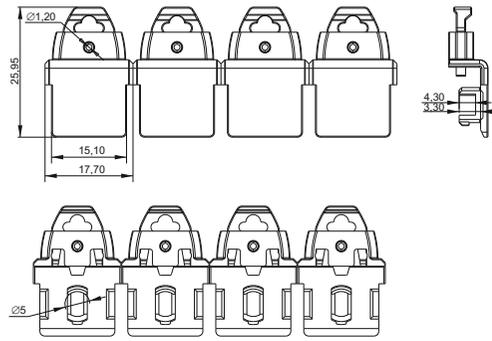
Габаритные размеры заглушки / Figure 2 – Overall dimensions of the blanking plug
